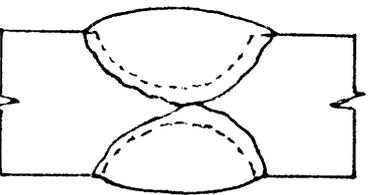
TIPOS DE SOLDADURAS (REF. 2)
